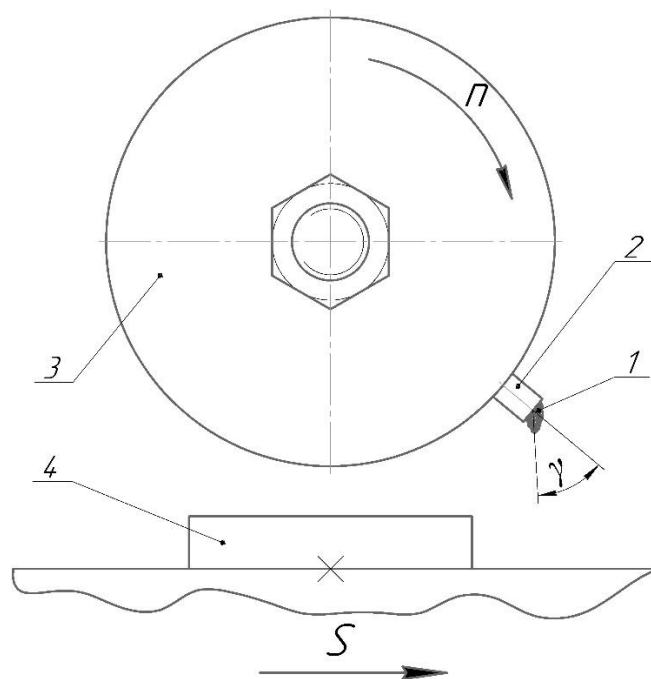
Приспособление для оценки режущей способности единичных зерен
